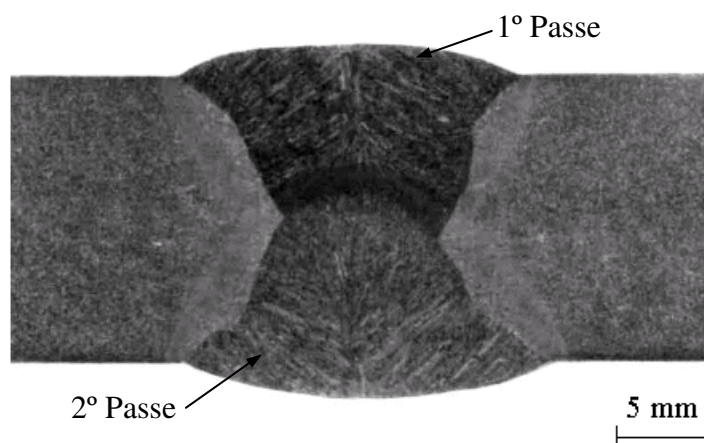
Macrografia da junta soldada. Ataque: reativo de iodo.
